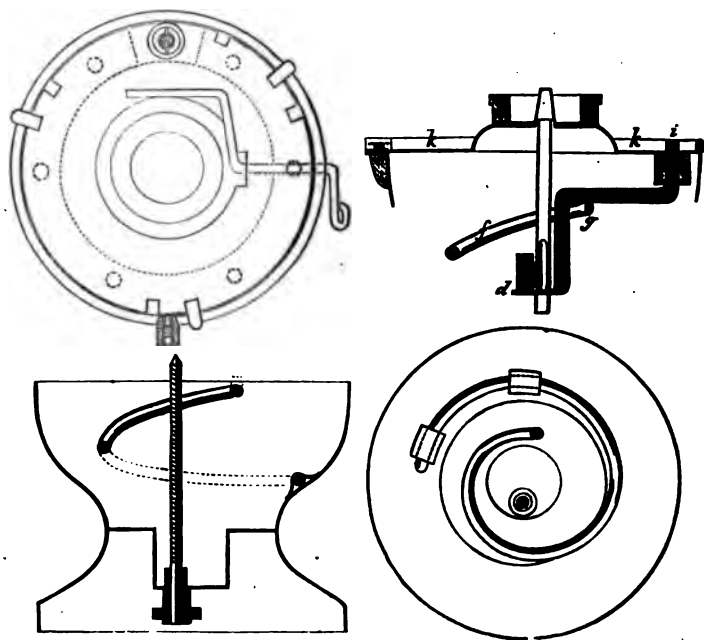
Plan et coupe de la lampe Dubrulle indiquant la disposition du porte-mèche, du ressort et de la fermeture.
